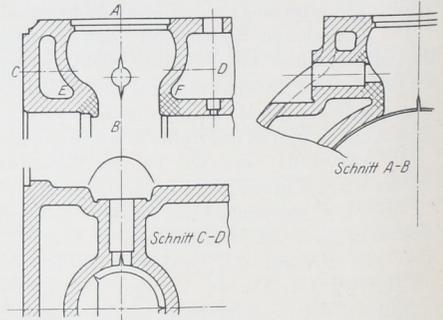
Zwiebelrisse an Großgasmaschinenzylindern.
